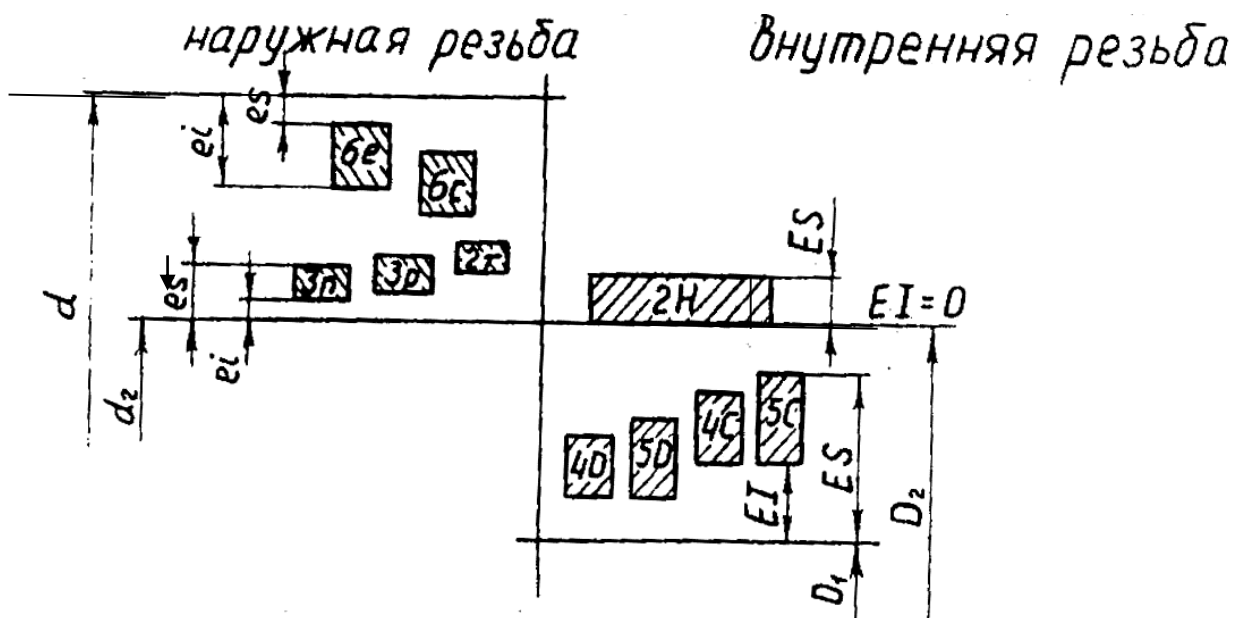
Схема расположения полей допусков резьбовых деталей с натягом
